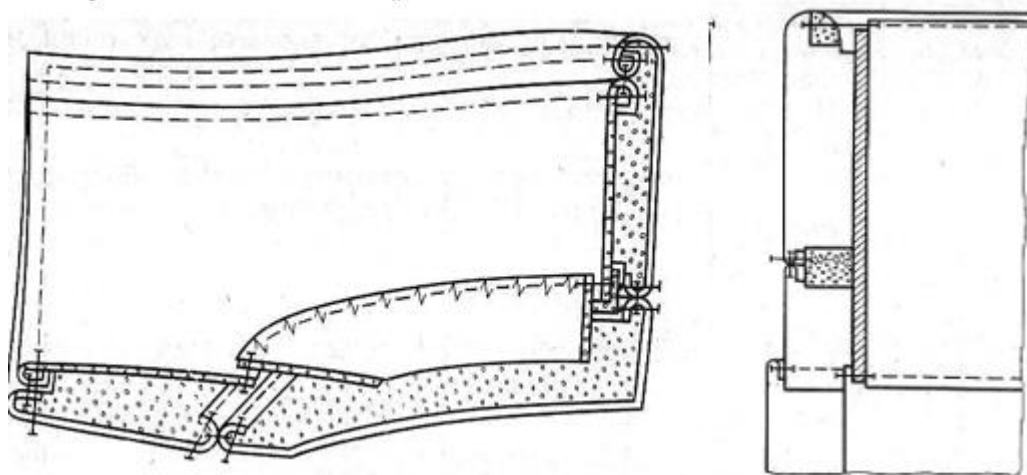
Схема сборки воротника пальто/пиджака
